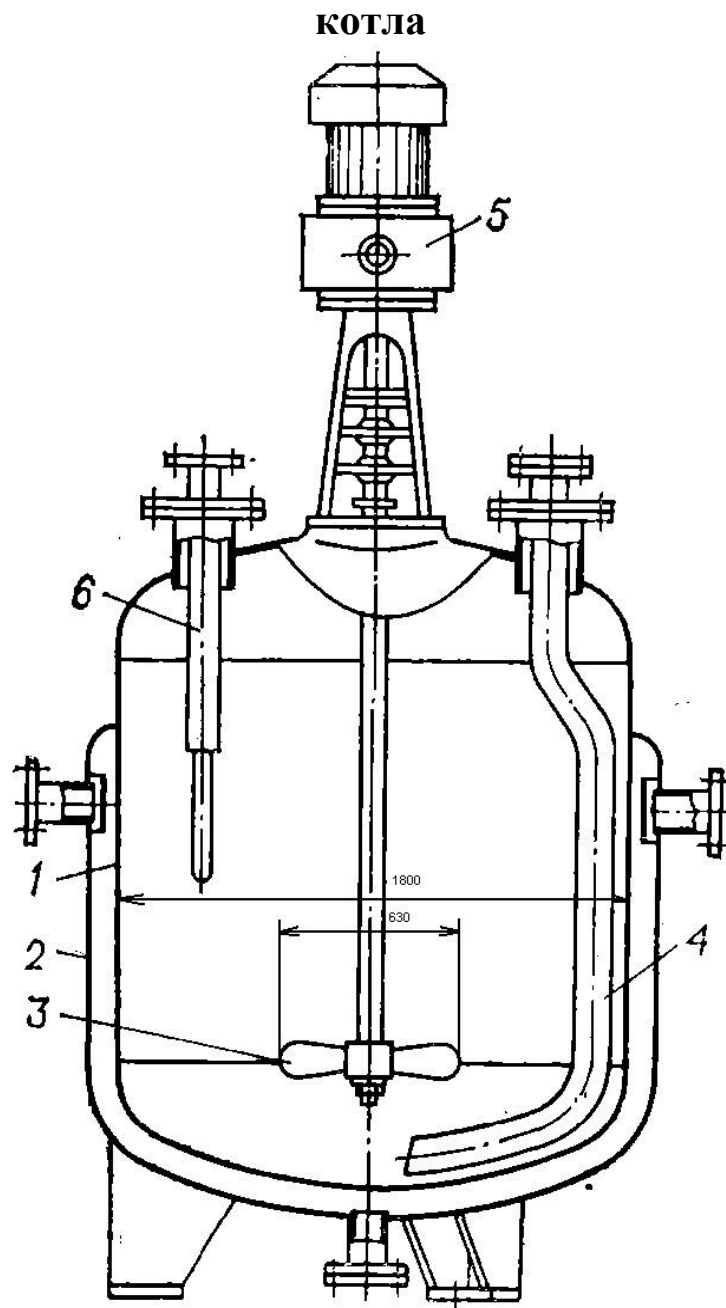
Реактор-котел: 1 – корпус; 2 – рубашка; 3 – мешалка; 4 – подача среды; 5 – привод; 6 – приборы контроля за процессом (термометр, манометр)
